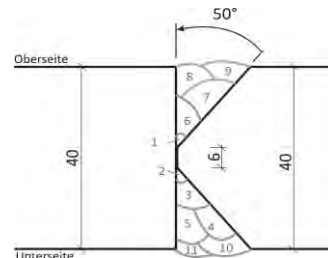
Schweißparameter der Probeschweißung Nr. 2
